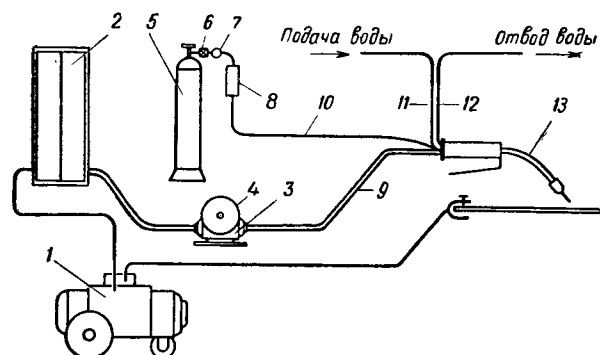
Полуавтоматическая установка для сварки в углекислом газе
